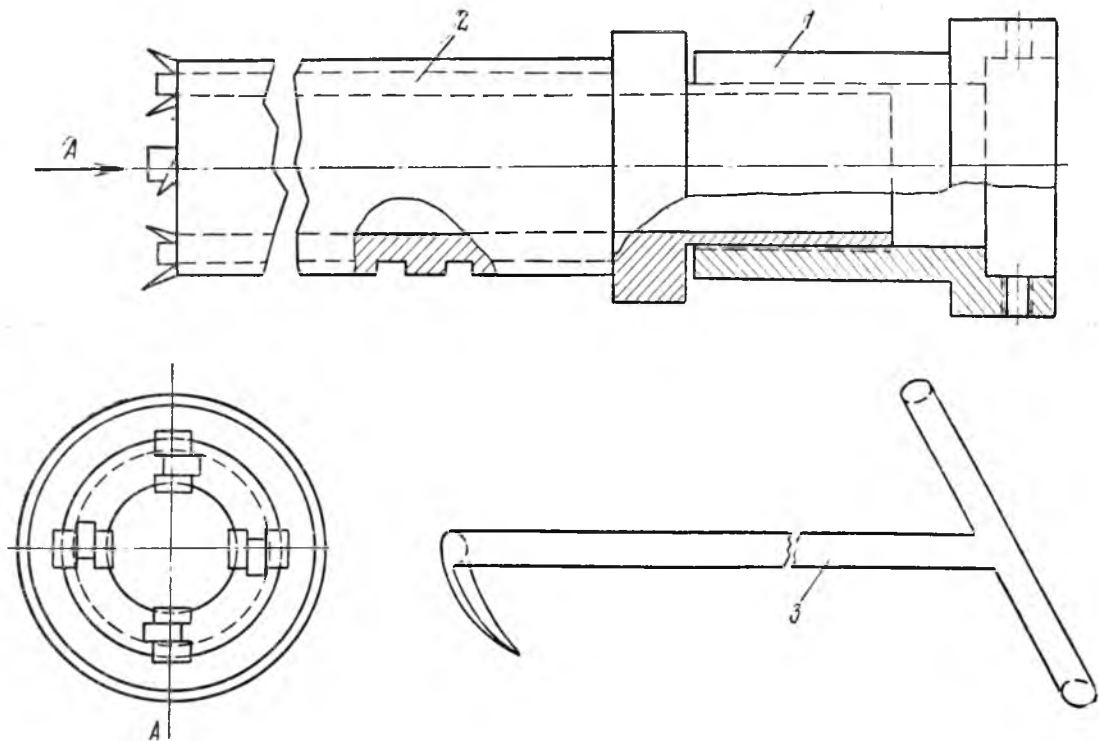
Схема механического бура и эскиз специального крюка для извлечения образцов
